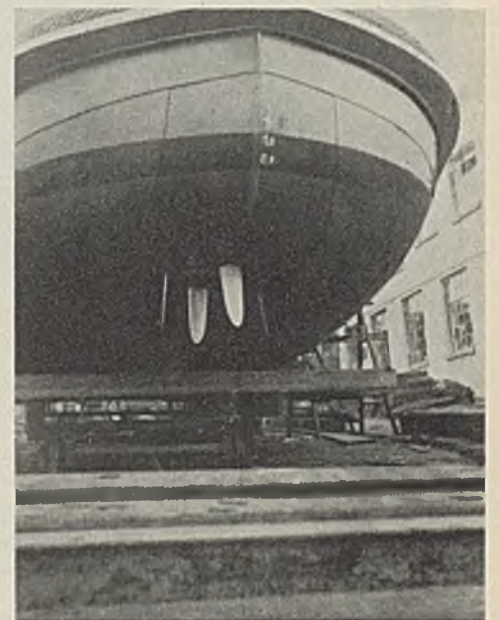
Heckansicht mit fertig eingebautem Propeller.
